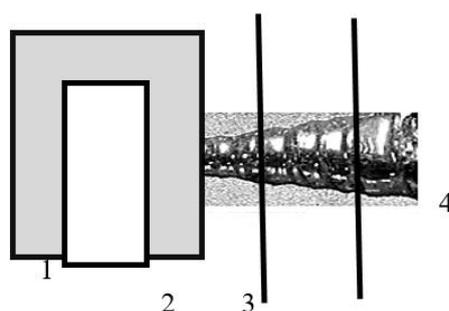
Схема формирования конической поры: 1 – холодильник, 2 и 3 – положение стенки подшипника, 4 – вид растущей конической поры
